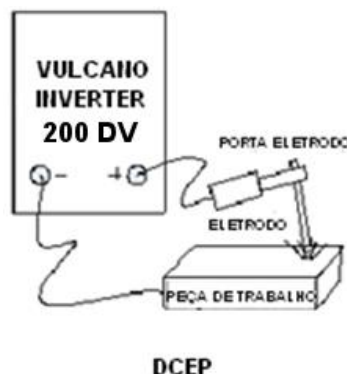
Conexão positiva para soldagem com eletrodo revestido
